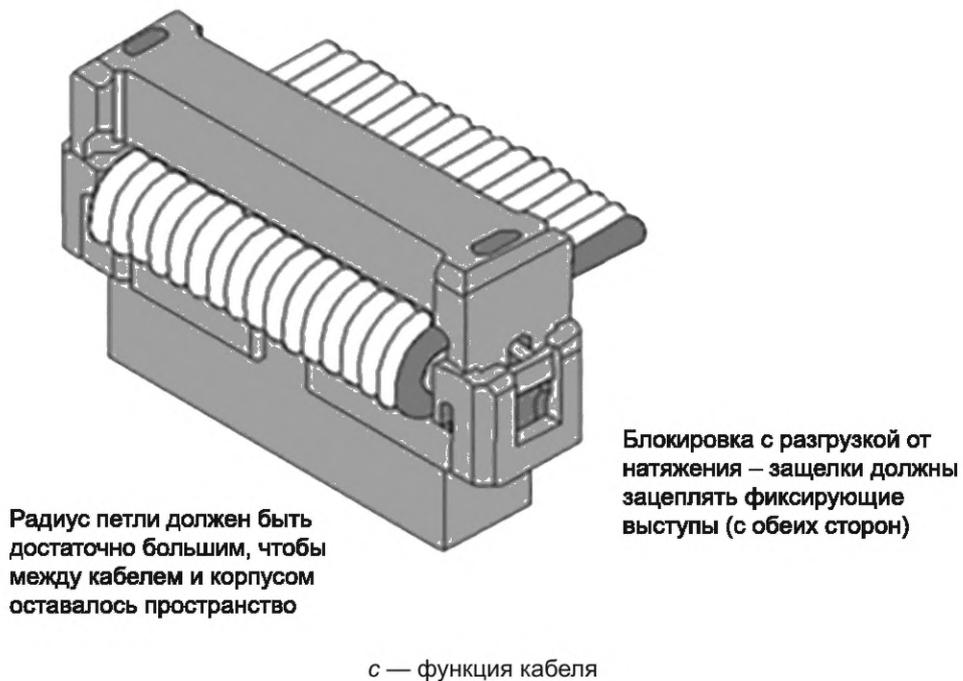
Детали корпусов разъемов для обеспечения правильного СПИ (примеры)
